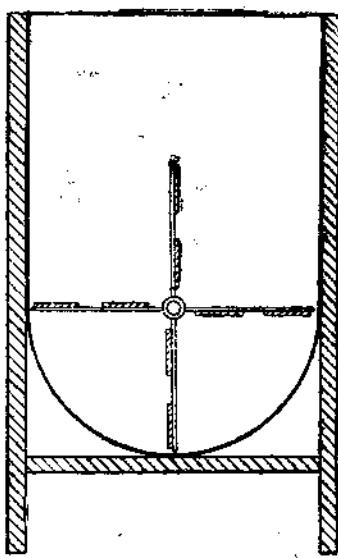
Деревянная мешалка для растворения фанерного клея. Вертикальный разрез.
